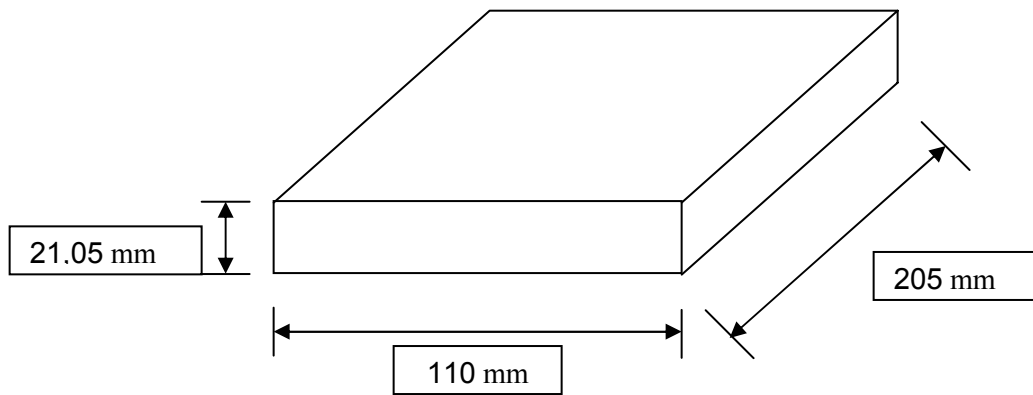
MEDIDAS EN MILÍMETROS DEL MOLDE DE FORMADO SIN MAQUINAR
